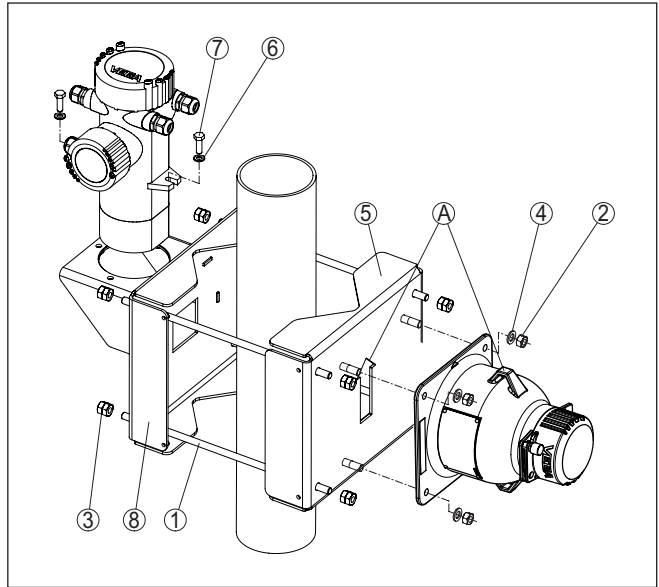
Klemmvorrichtung mit senkrecht montiertem Sensor (mit VEGASOURCE 81, 82, 83)
